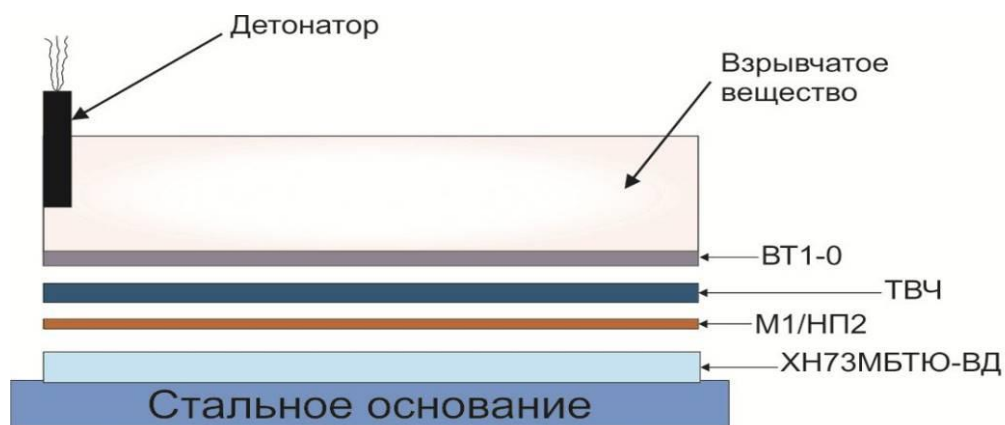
Схема сварки взрывом четырехслойных композитов
